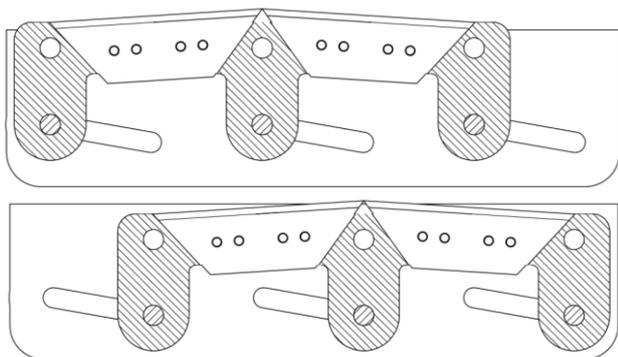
Нижнее а и верхнее б положения механизма вертикального реза для твердых пород древесины
